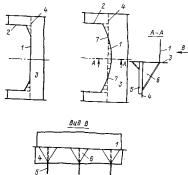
Подкрепление палубы у лобовой стенки корытовой надстройки
